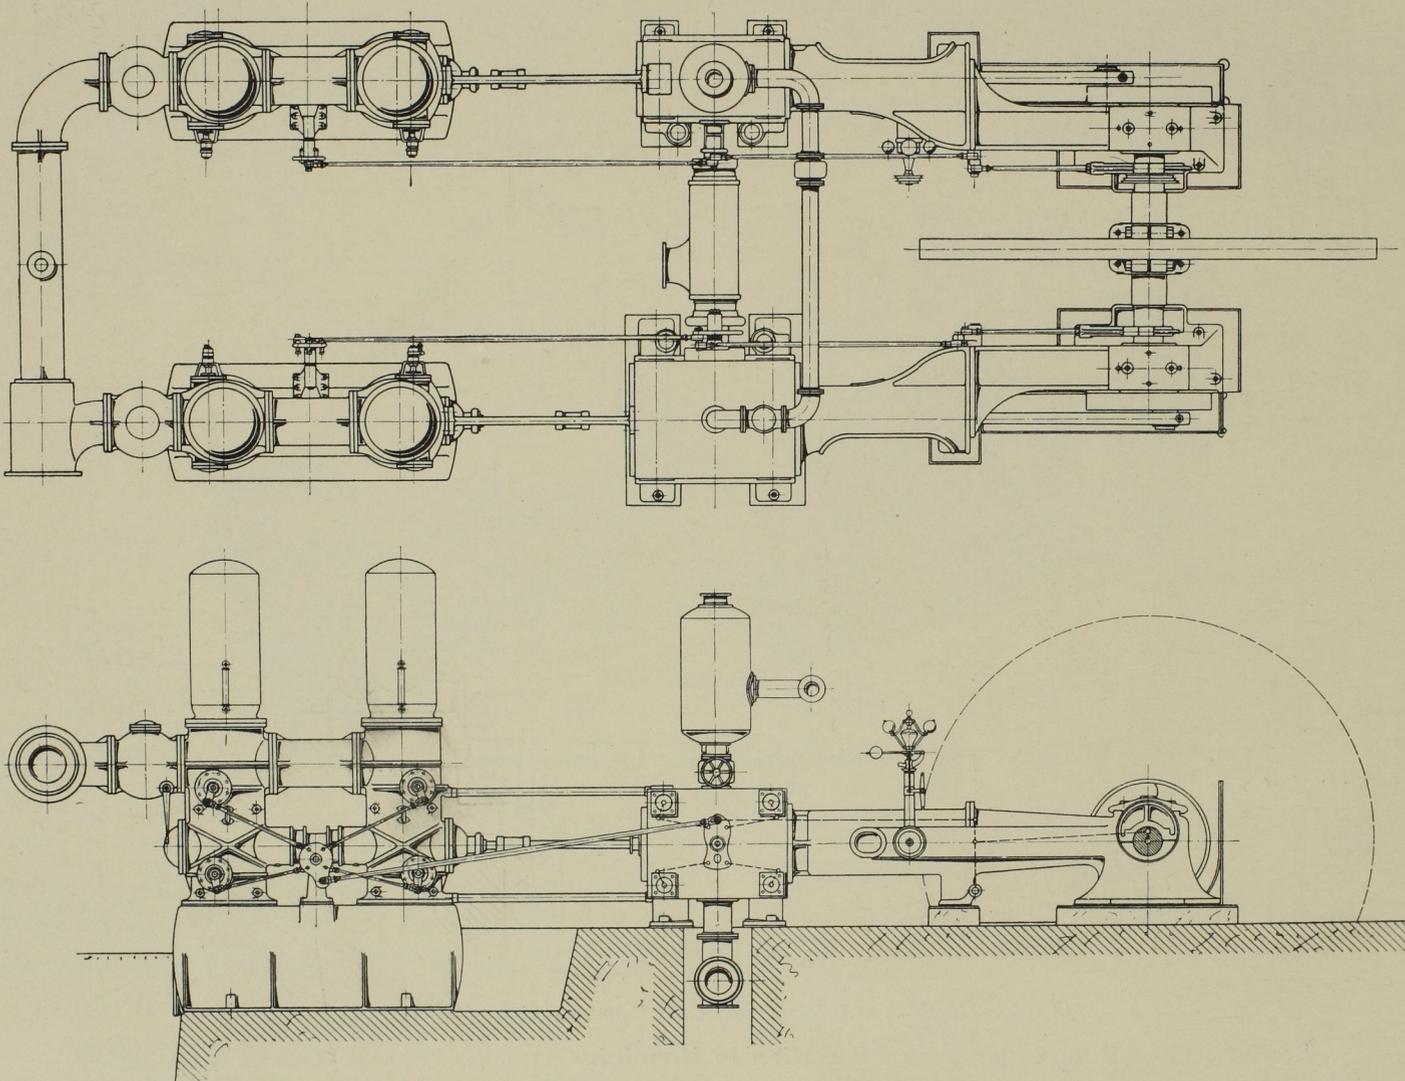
Grundriss und Seitenansicht. Massst. 1:96.
